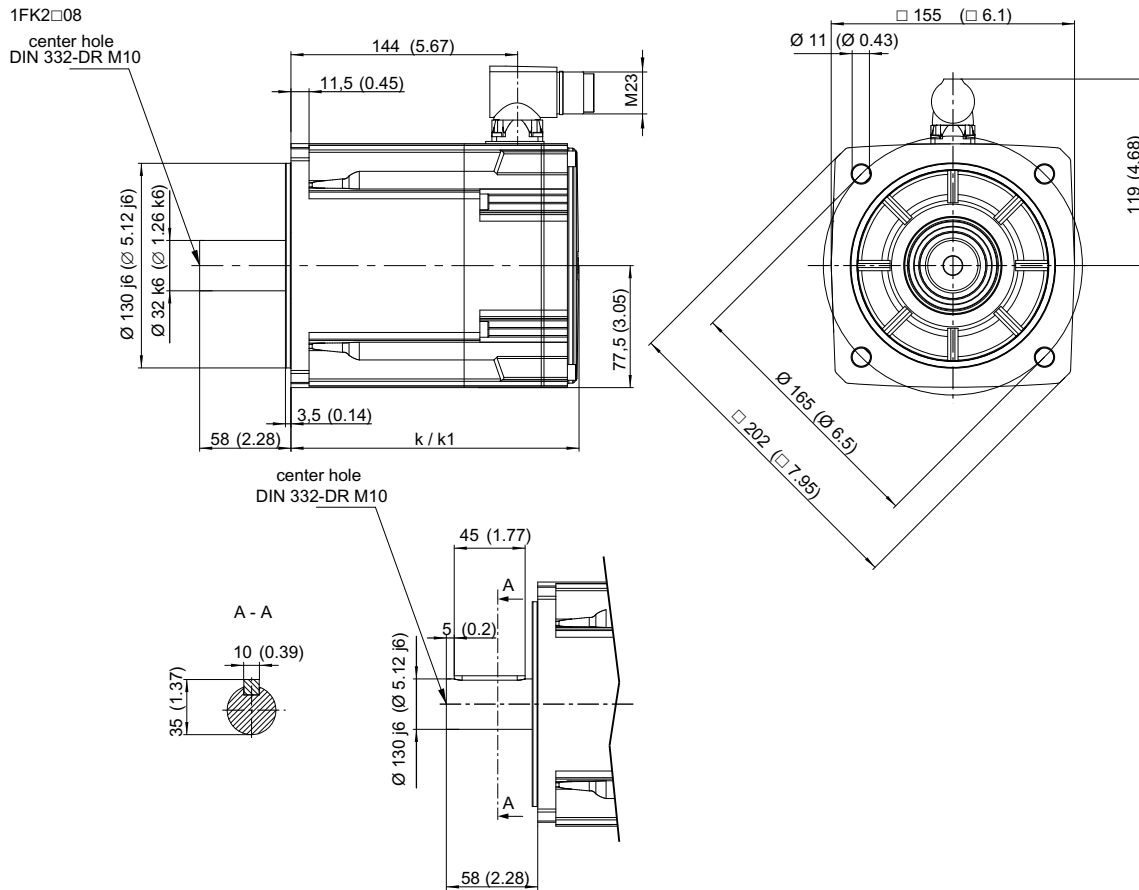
Maßzeichnung_1FK2208-3AF00_OCC
